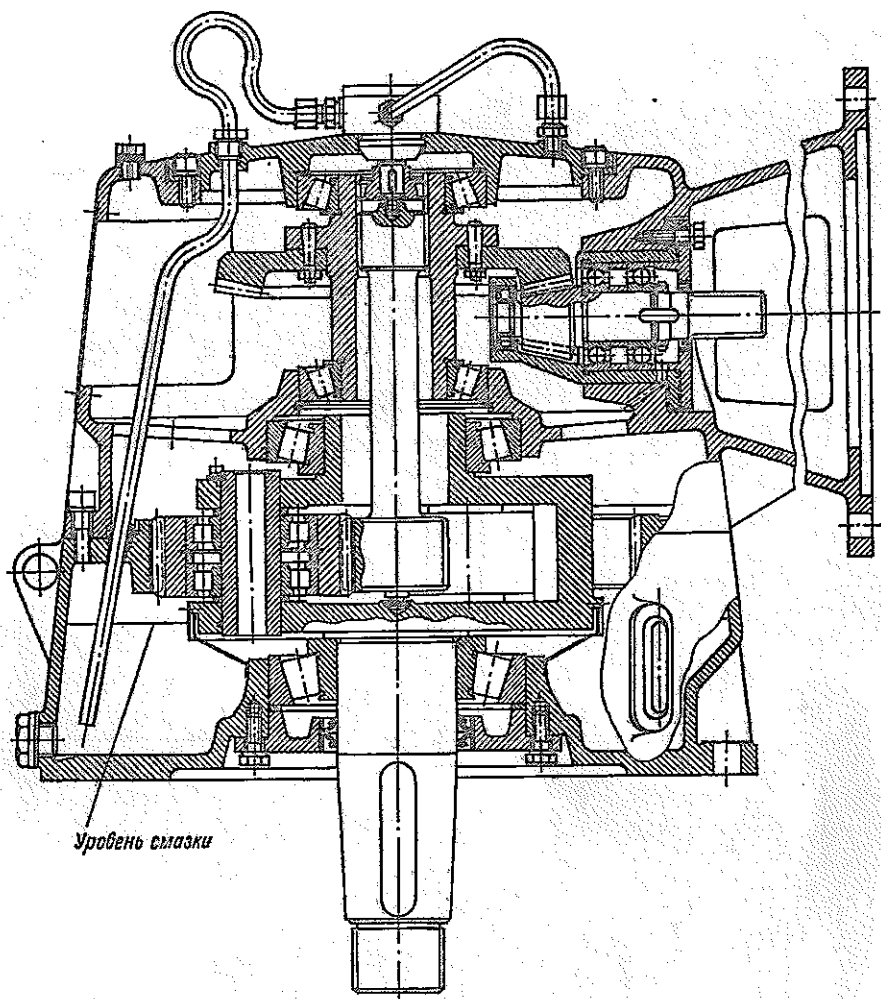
Двухступенчатый редуктор с конической быстроходной и планетарной тихоходной ступенями
